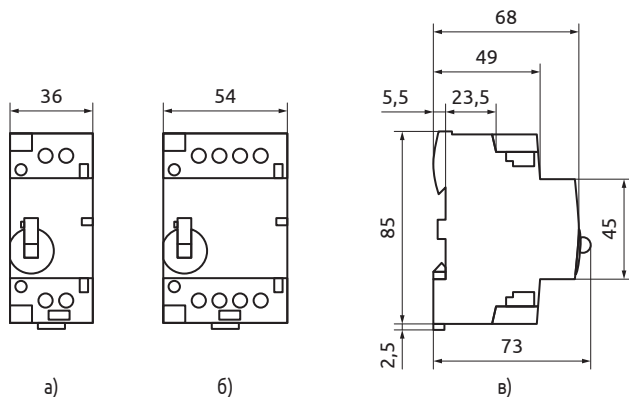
Габаритный чертеж контакторов АСМ-М на токи от 40 до 63 А:
